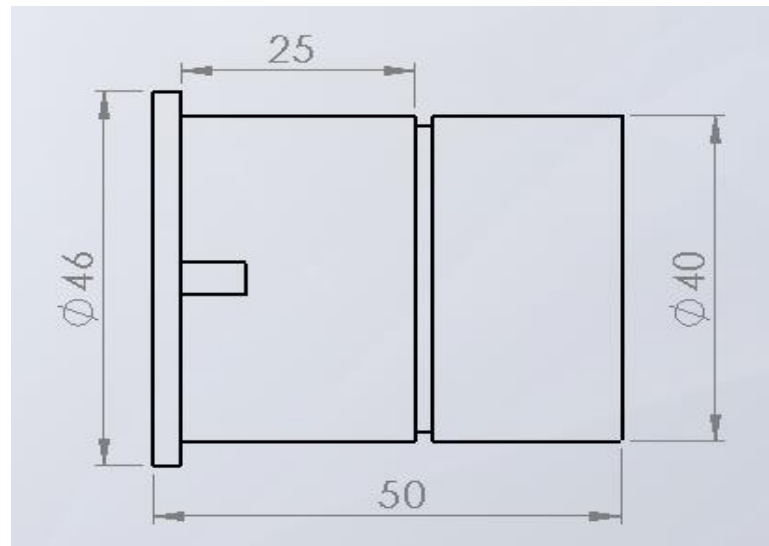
Casquilho com roscado interior e dimensões (mm)
